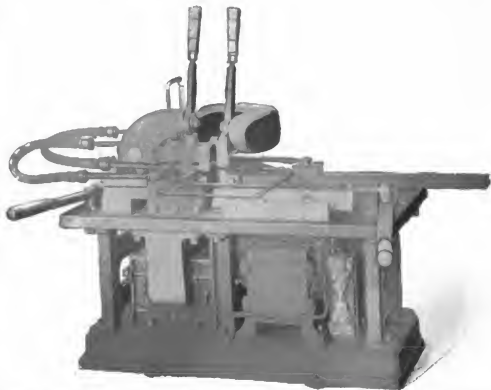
Schweissapparat 10 A, eingerichtet zum Schweissen unter einem rechten Winkel.
